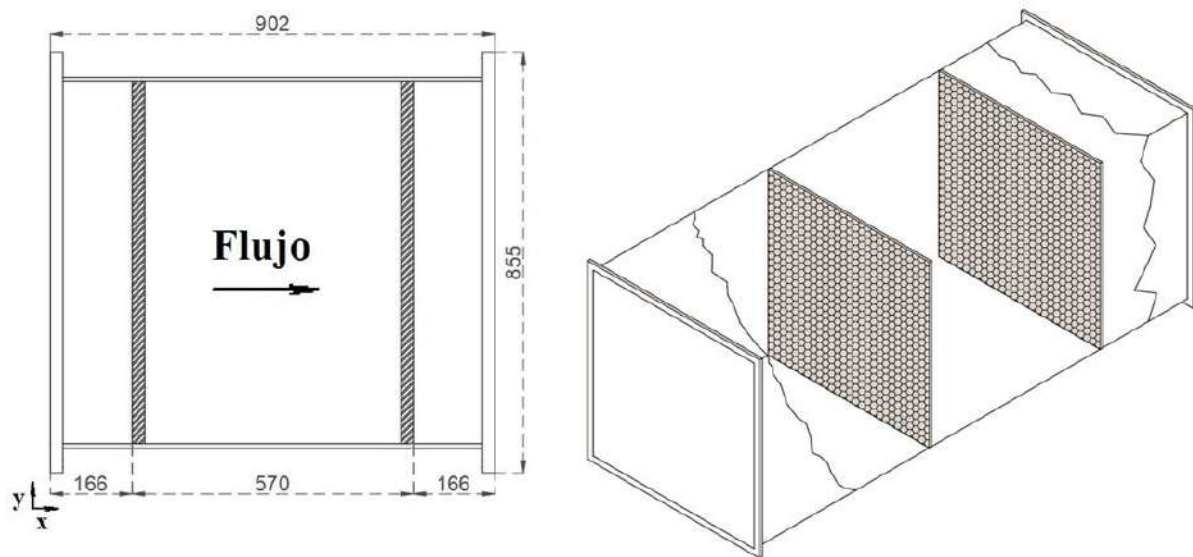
Distribución da paneles en cámara estabilizadora (acotada en mm).
